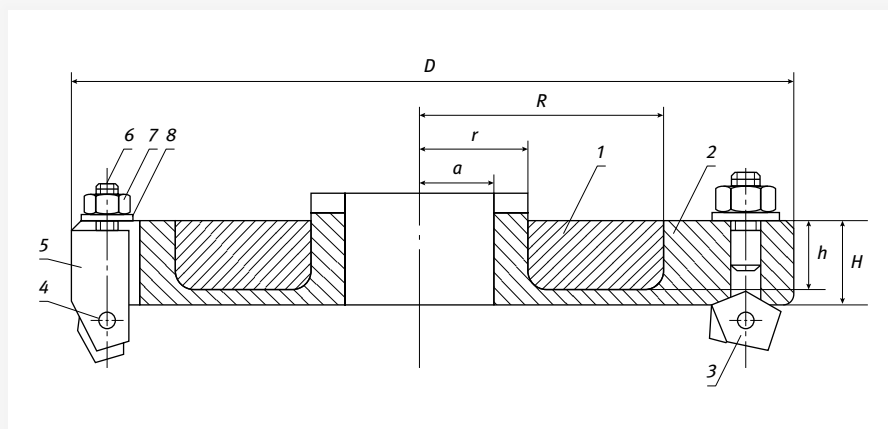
Торцевая фреза с корпусом, содержащим композит на основе бетона [1, 9]: 1 – кольцеобразная вставка, заполненная композитным материалом; 2 – корпус; 3 – режущая пластина; 4 – штифт; 5 – державка; 6 – гайка; 7 – шайба
